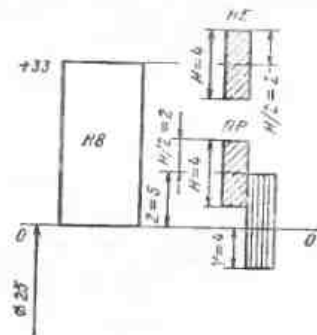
Схема распределения полей допусков калибров для размера 25H8
